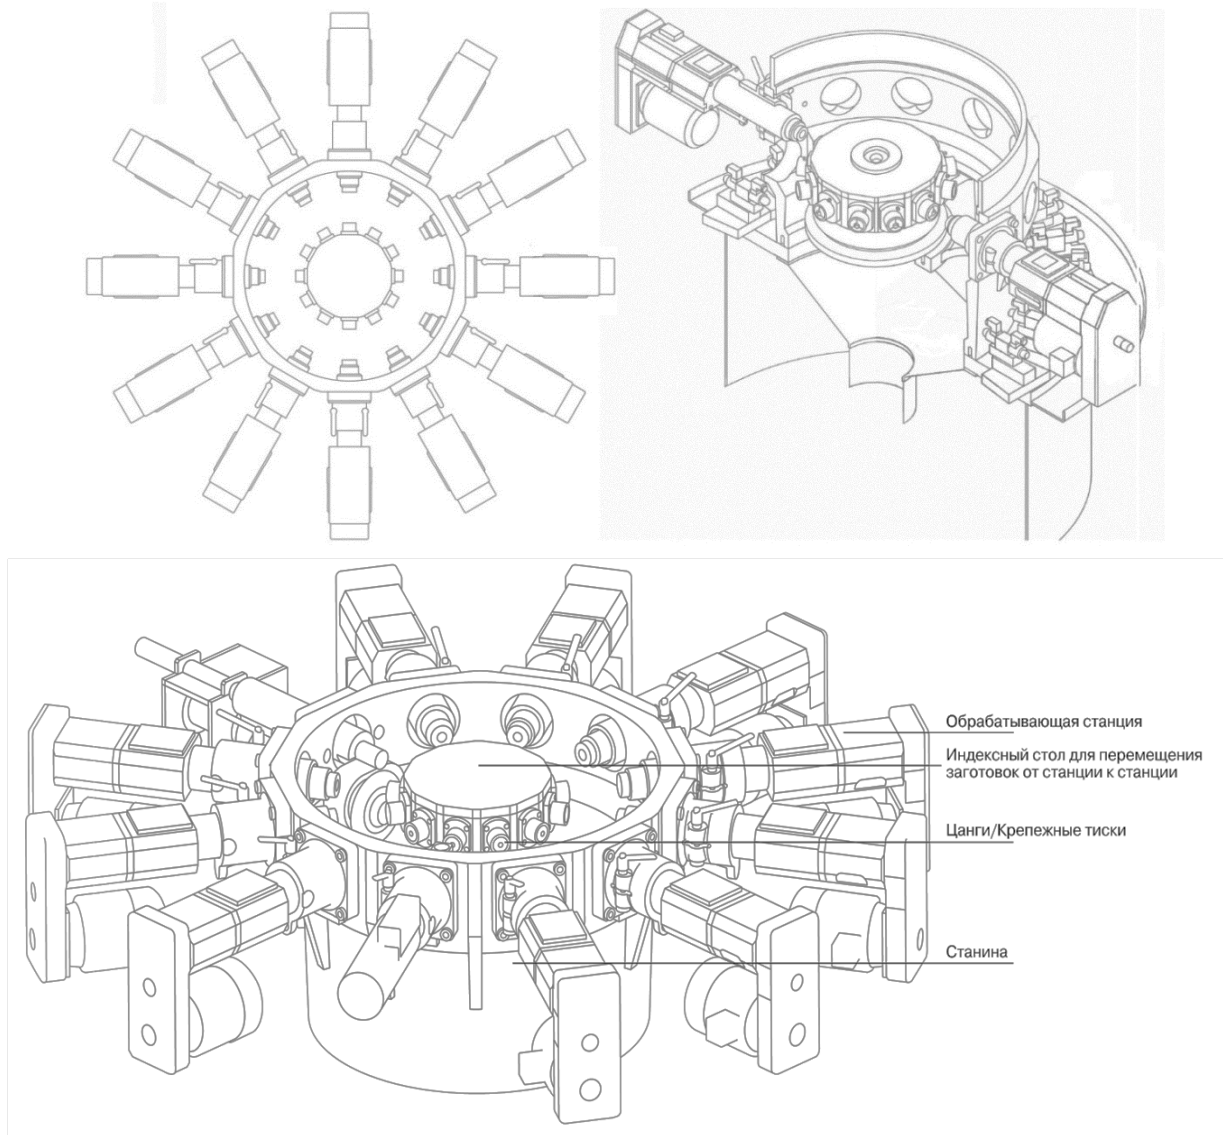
Компонування агрегатного верстата НВ 32/16
